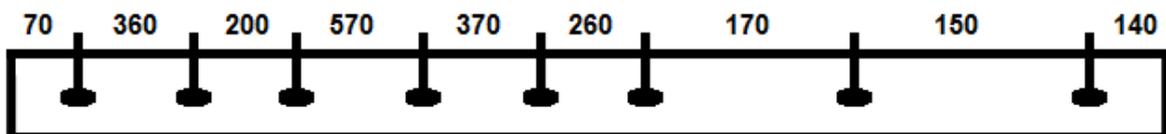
Perfil “U” superior – Lado externo – Vista frontal - fixação do trilho no perfil “U”
